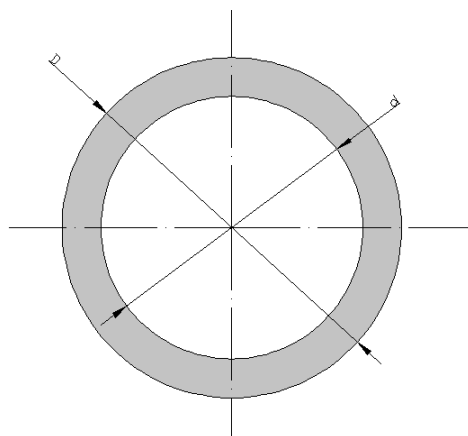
Perfil de la columna para el caso de grúa sin contrapeso.
